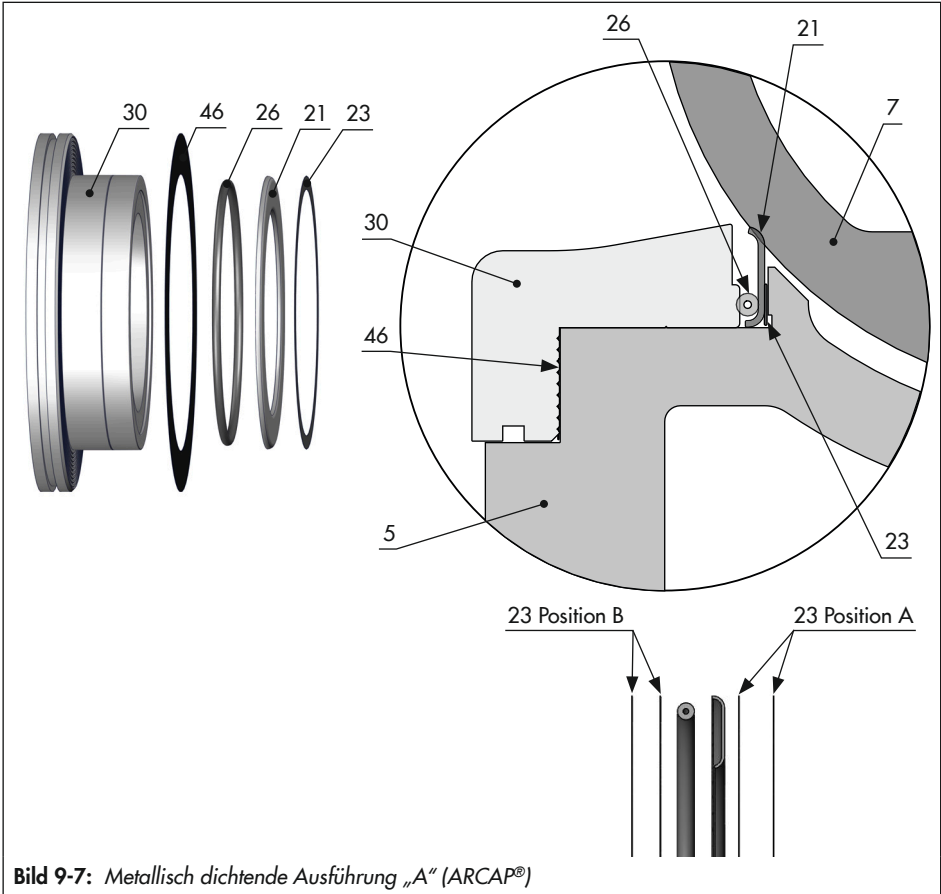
Metallisch dichtende Ausführung „A“ (ARCAP®)
